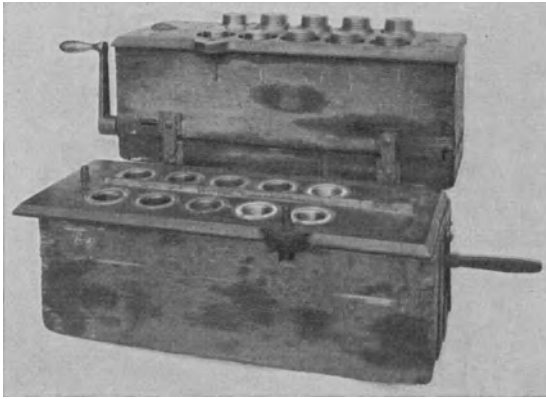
Einrichtung zum Formen nahtloser Gewinde.
